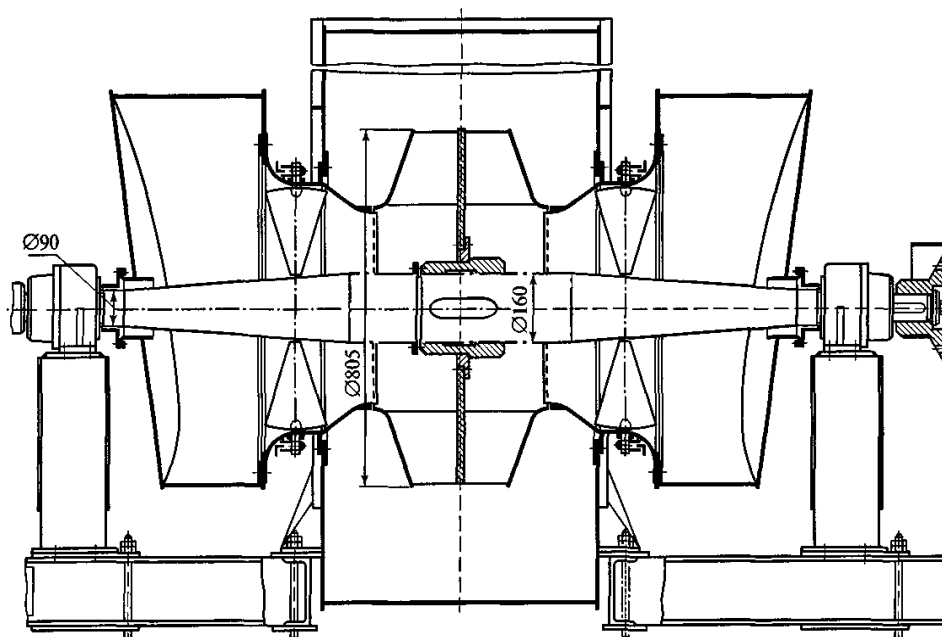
Конструкция центробежного вентилятора двустороннего всасывания
